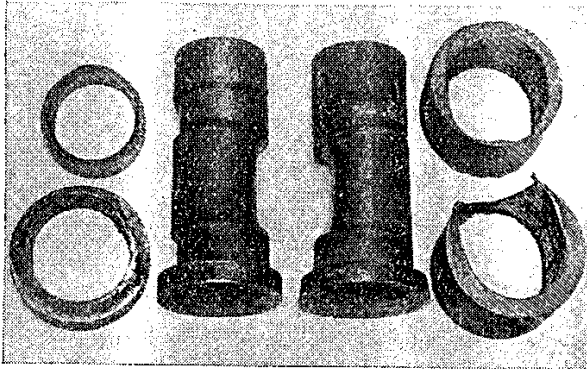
Stark abgenutzte Bolzen und Buchsen der Ausgleichsmechanik einer Lokomotive
